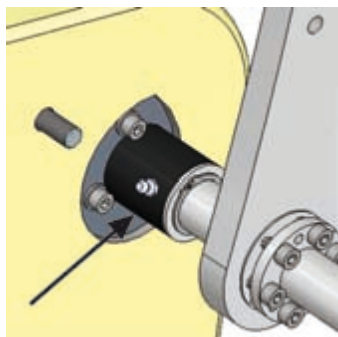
Втулка вала управления (смазывание через ниппель или автоматическая смазка)
